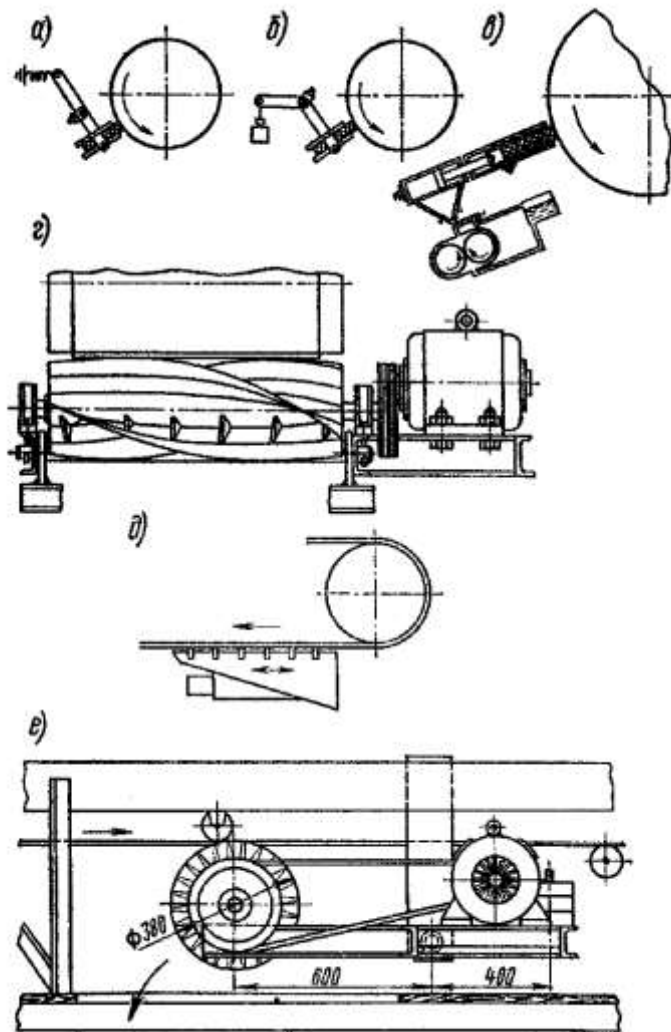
Схемы установки механических устройств для очистки ленты:
